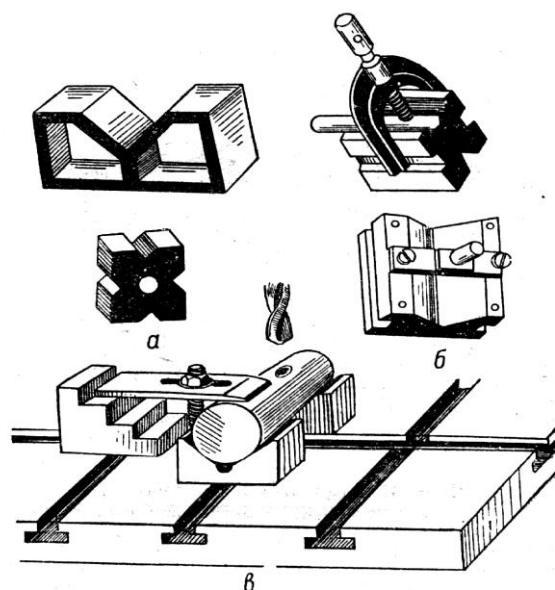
Пристосування для закріплення циліндричних заготовок при свердлінні: а — призми; б — струбцини; в — приклад закріплення валика на столі свердлильного верстату
